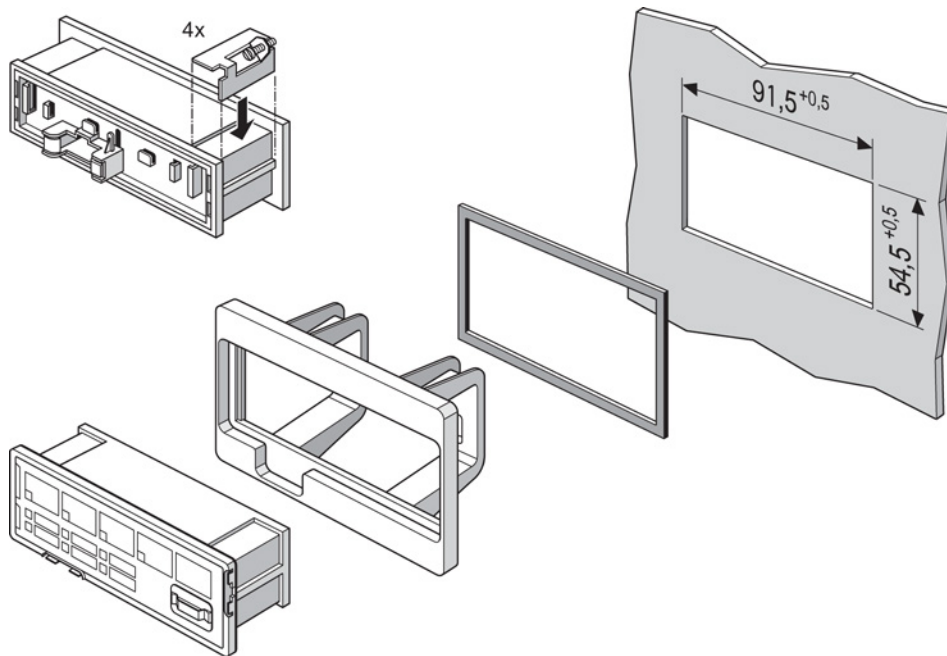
Montage de l'adaptateur pour module frontal (1)
